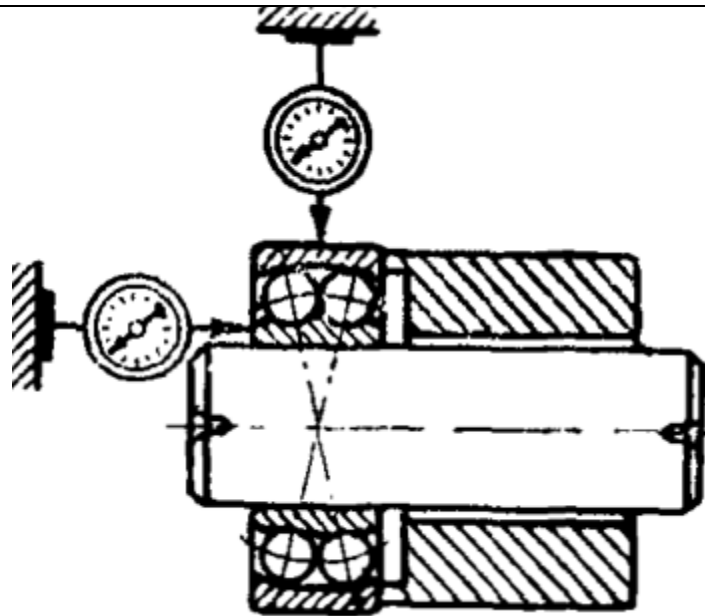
Проверка биений сферических подшипников на оправке с опорной втулкой.
